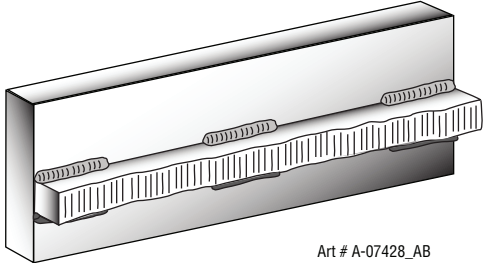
Soldadura discontinua con cordones paralelos
